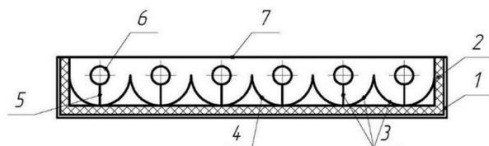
Поперечний переріз сонячного колектора: 1 – корпус СК; 2 – теплоізоляція; 3 – абсорбер; 4 – циліндричний сегмент; 5 – ребро; 6 – теплова труба; 7 – скляна кришка
